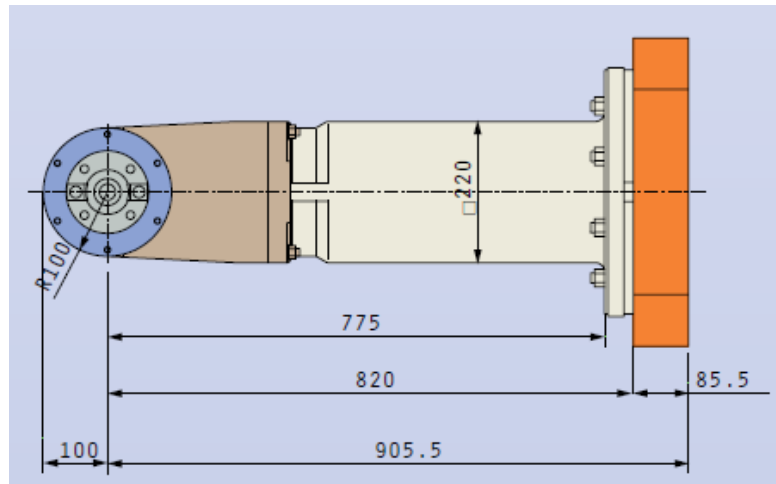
Prodloužená frézovací hlava KF-2/90 [21]
